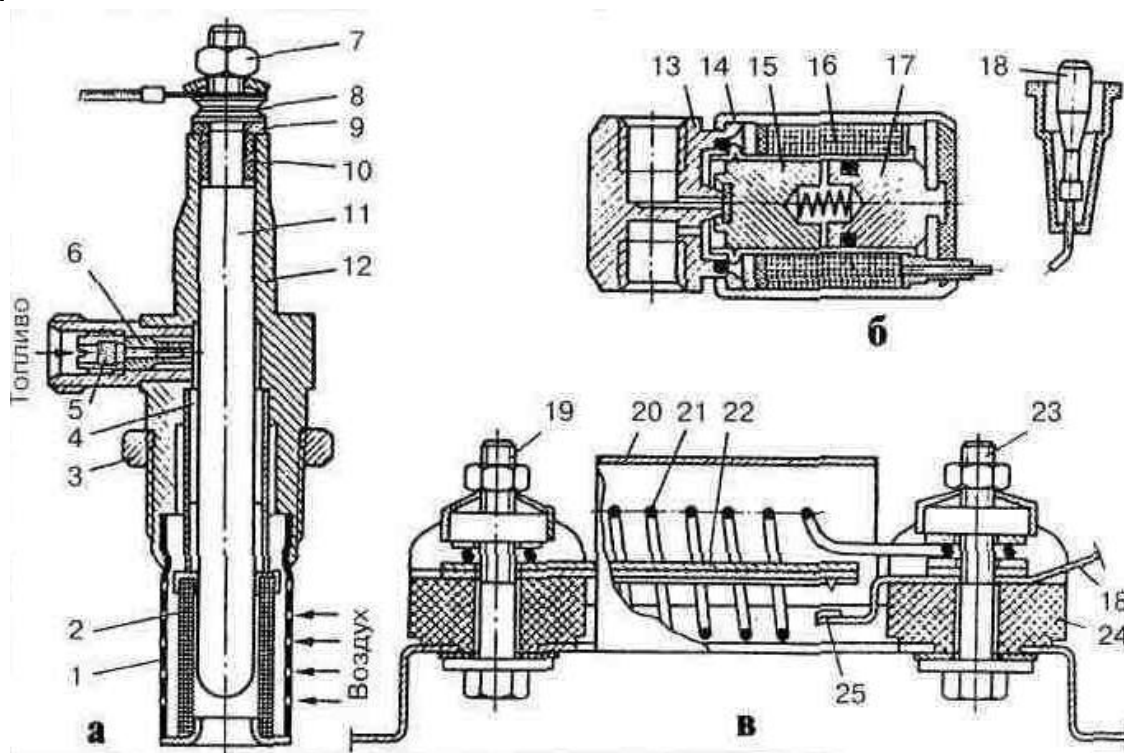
устройства для облегчения запуска: а - факельная штифтовая свеча, б - электромагнитный топливный клапан, в-добавочный резистор с термореле,
